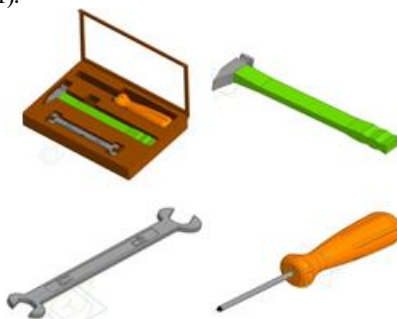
Сборка ящика с инструментами в КОМПАС-3D
